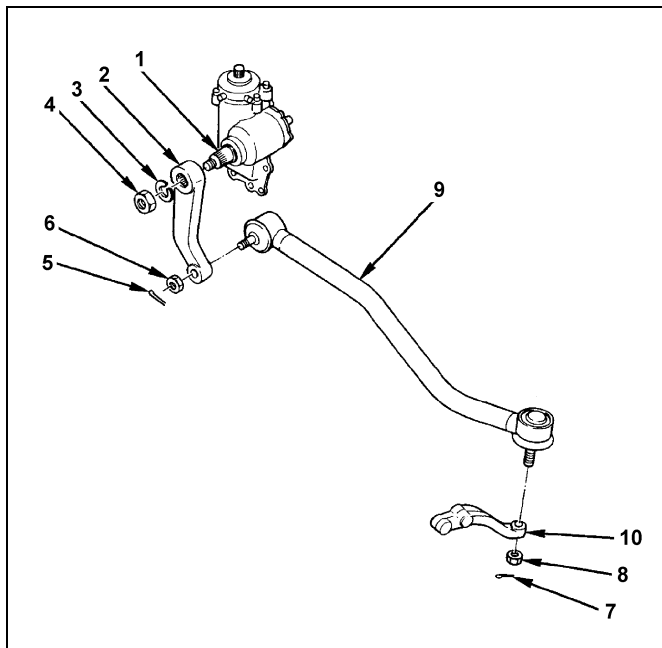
Рулевая сошка и продольная рулевая тяга. 1 - выходной вал рулевого механизма, 2 - рулевая сошка, 3 - пружинная шайба, 4 - гайка рулевой сошки, 5 - шплинт, 6 - гайка, 7 - шплинт, 8 - гайка, 9 - продольная рулевая тяга, 10 - поворотный рычаг.
